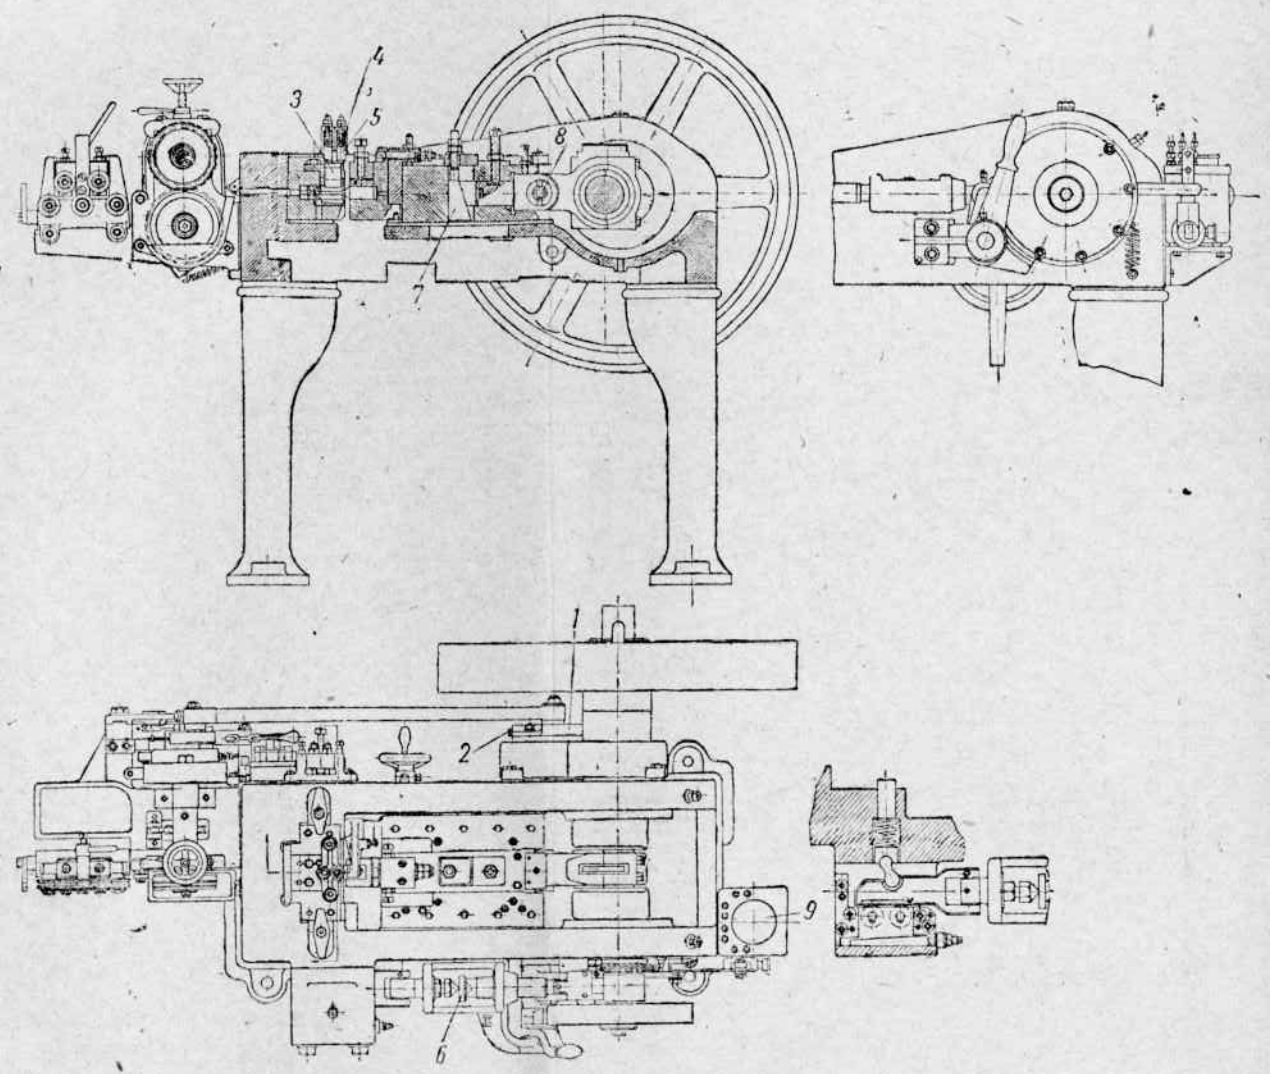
а. Двухударный холодновысачочный автомат с цельной матрицей фирмы Кизерлинг мод. DN3-9. Вид со стороны прибора выталкивания и поперечный разрез
